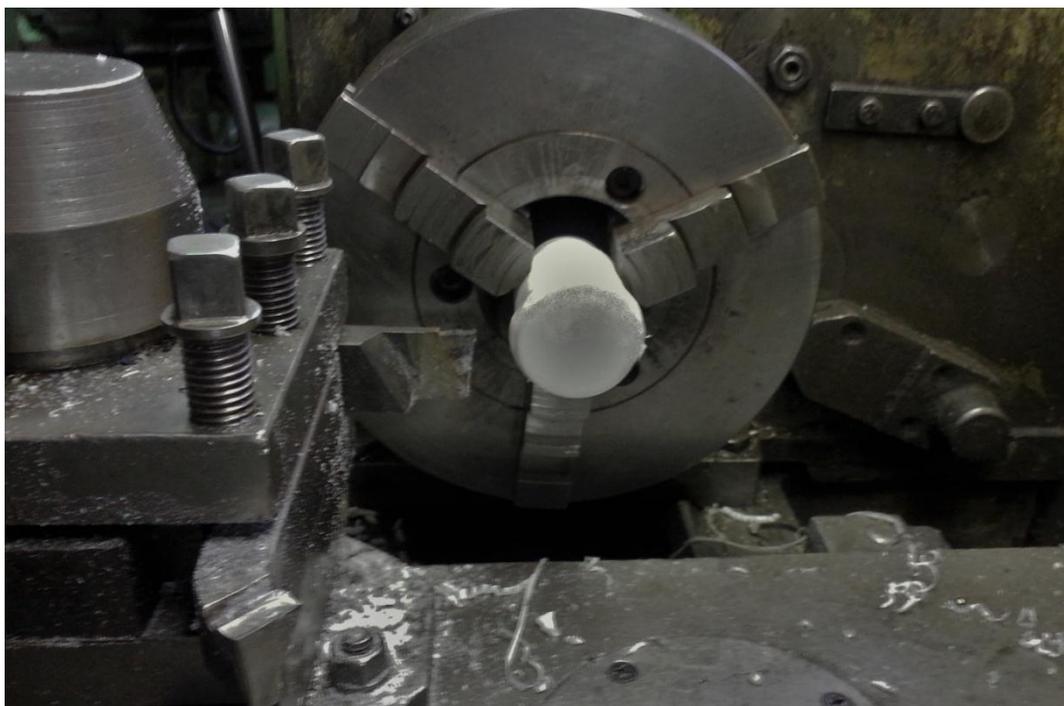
Процесс изготовления фторопластового переходника на токарном станке
